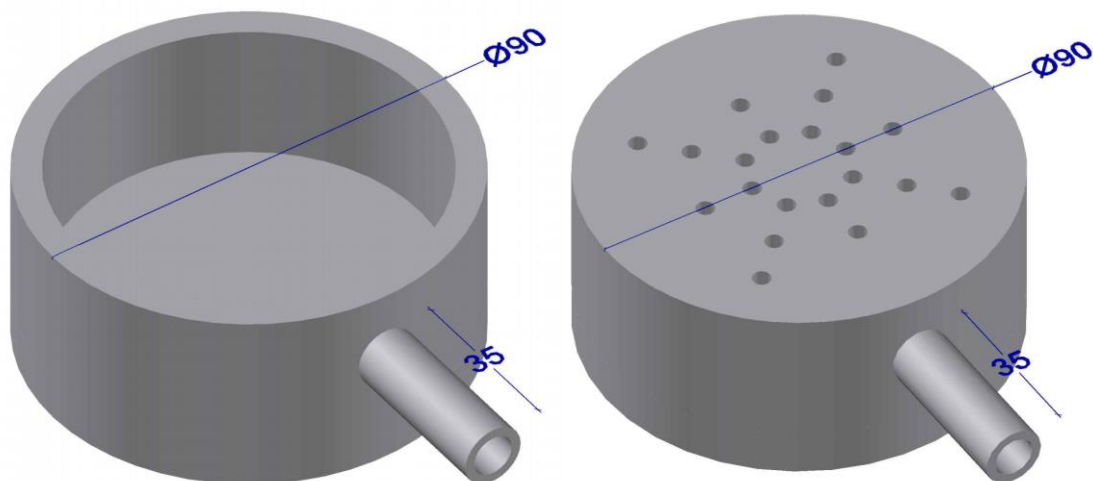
Modelado del difusor. Vista superior. Representación de dimensiones en milímetros. Primer modelado en AutoCAD del difusor.
